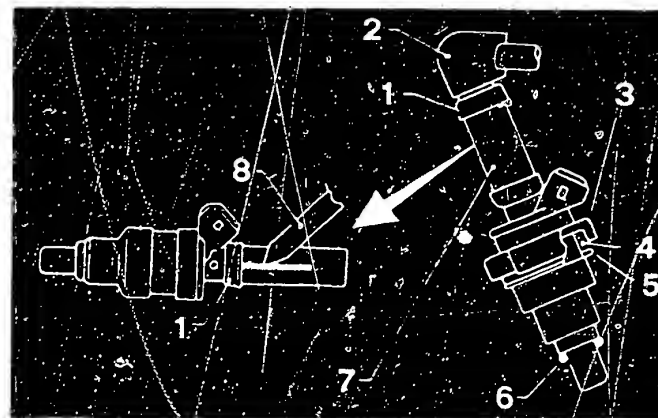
Um den Benzinschlauch vom Einspritzventil zu trennen ist der Schlauch vorsichtig mit einem Lötkolben (150W) aufzutrennen. 1 Hülse ring – 2 Kraftstoffleitung – 3 Einspritzventilhalter – 4 Gumidämpfer – 5 Sicherungsring – 6 O-Ring – 7 Schlauchanschluss – 8 Lötkolben.
